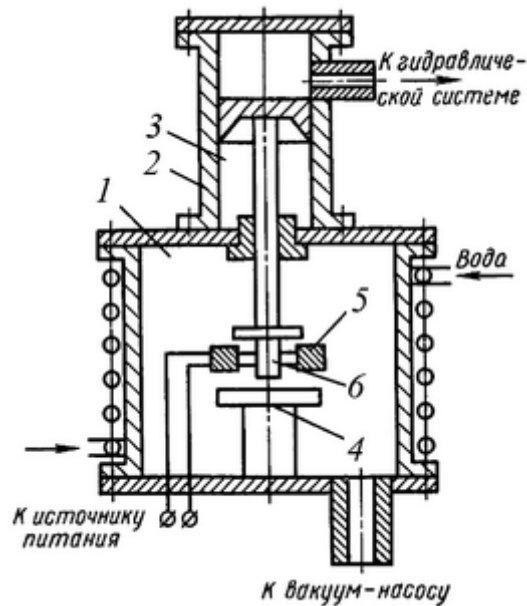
Принципиальная схема установки для диффузионной сварки в вакууме:
